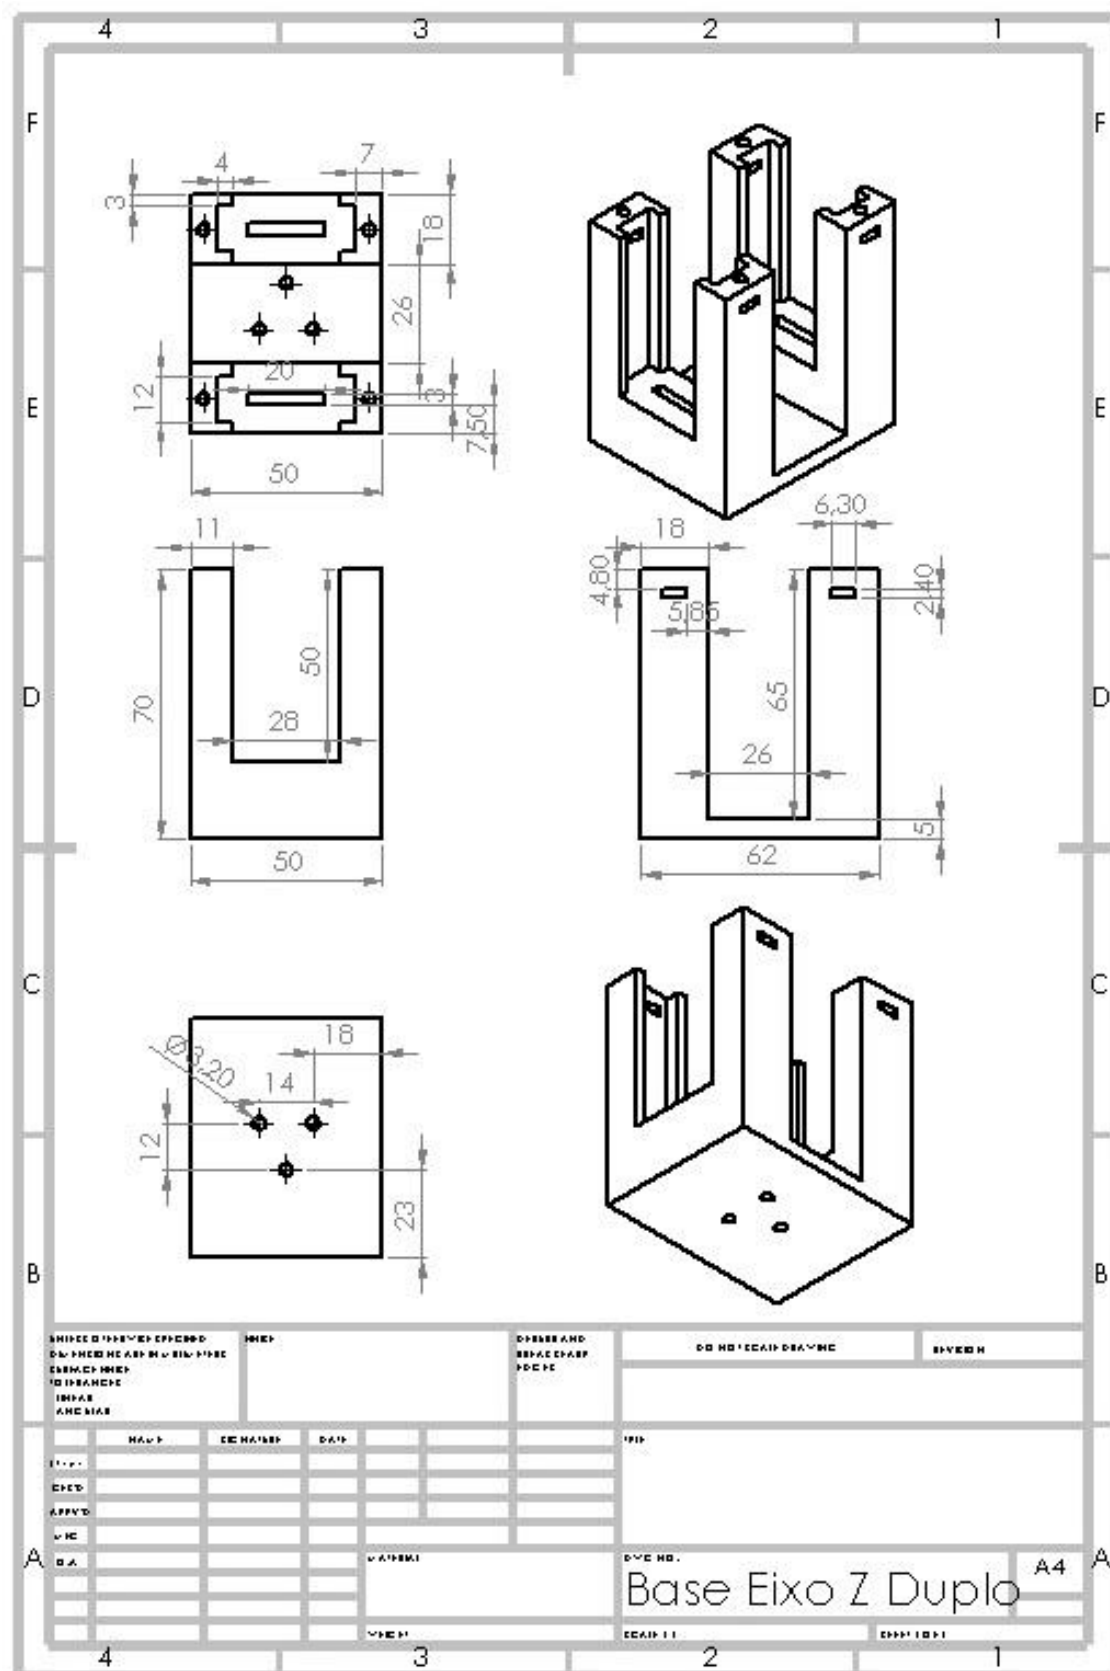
Desenho técnico da peça Base Eixo Z (Duplo)
